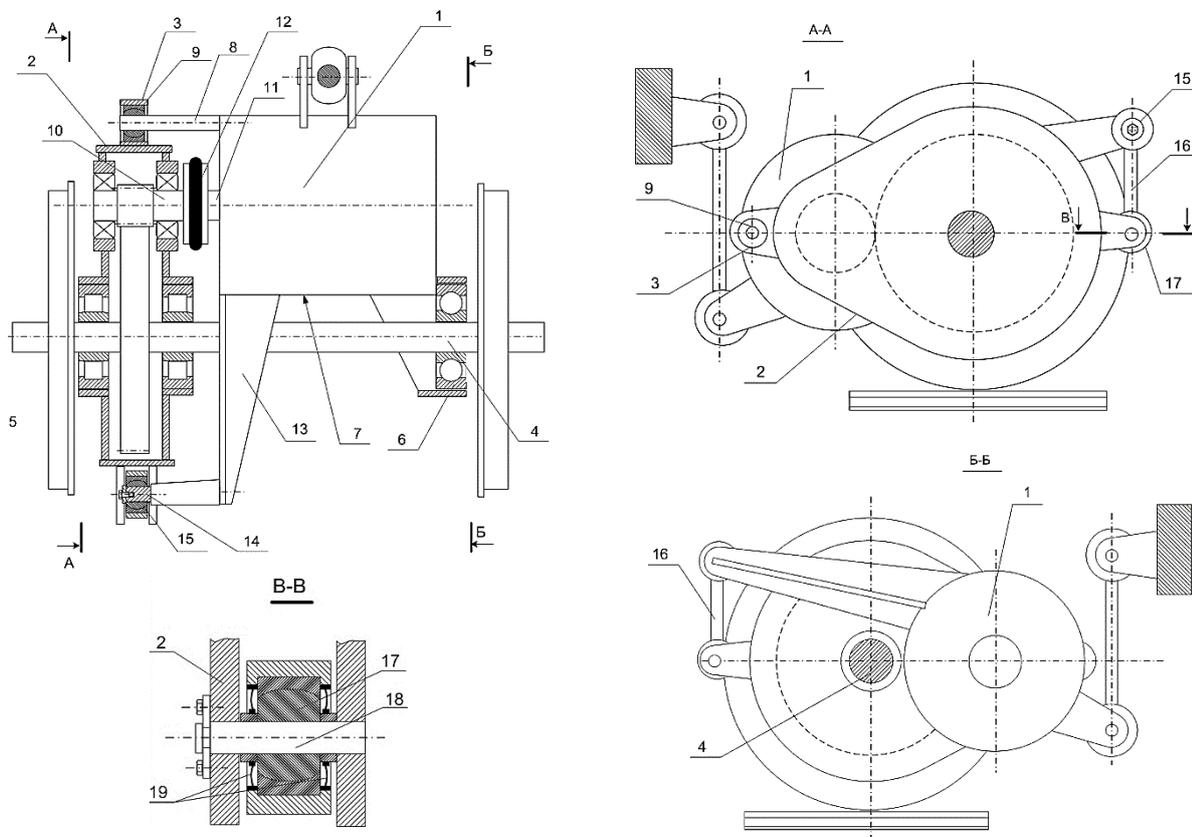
Вариант агрегатного тягового привода локомотива: 1 – ТЭД; 2 – осевой редуктор; 3 – разъемное соединение; 4 – ось колесной пары; 5,6 – подшипники; 7 – корпус ТЭД; 8 – палец; 9,15,17 – сферические шарниры; 10 – вал ТЭД; 11 – вал осевого редуктора;
